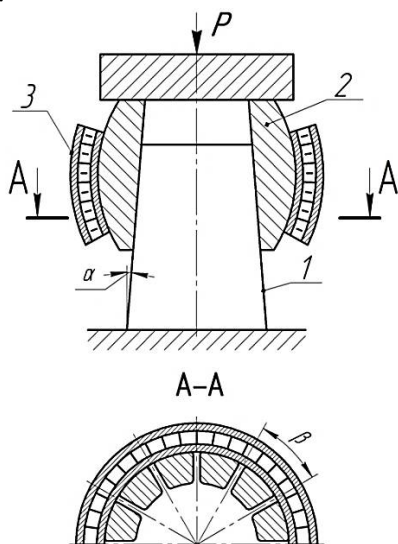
Формообразование оболочки разжимными пуансонами: 1 - конус; 2 - разжимной пуансон; 3 - заготовка
